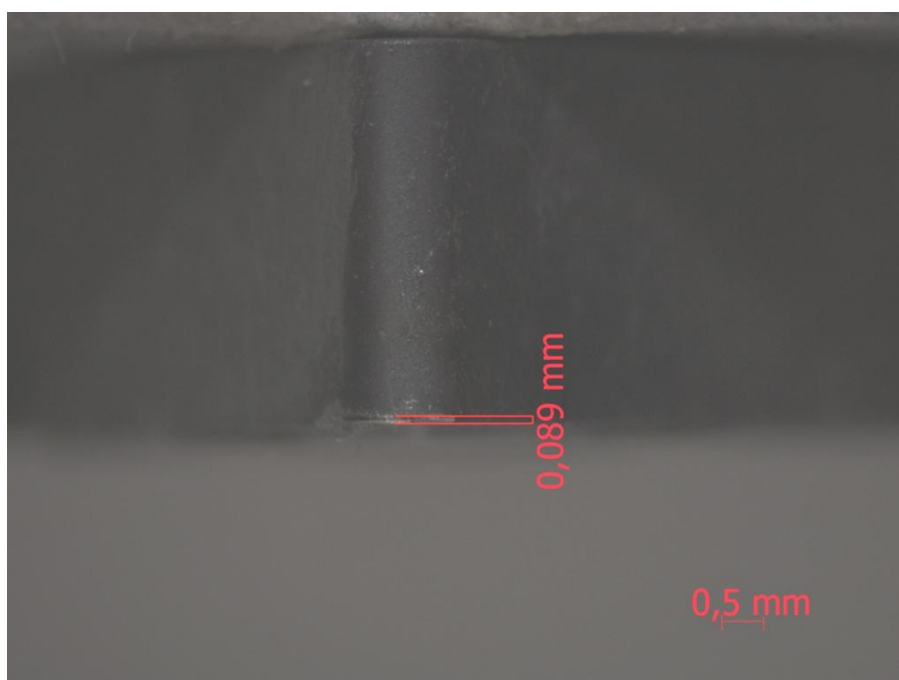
Desgaste de flanco Vc 100 5% de diluição
